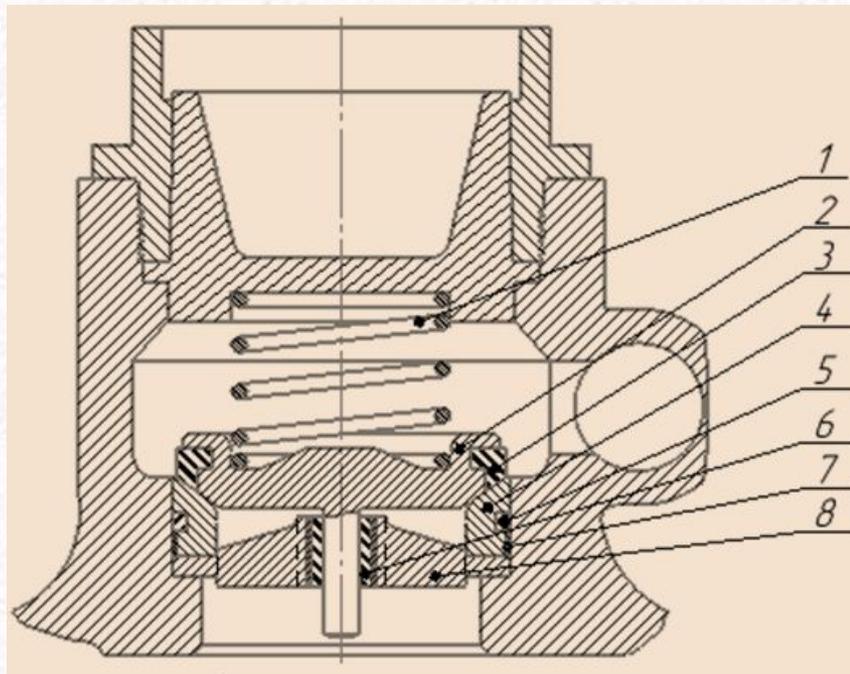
Клапан насоса (1 – пружина; 2 – корпус клапана; 3 – гибкая вставка; 4 – седло; 5 – уплотнительное кольцо; 6 – направляющее кольцо; 7 – фрикционная втулка; 8 – втулка)
